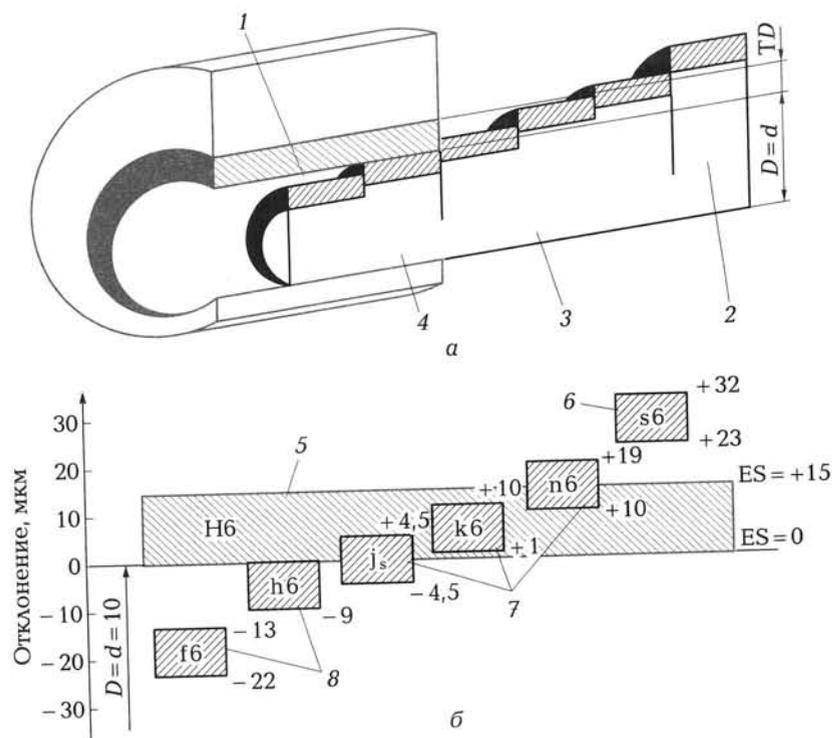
Расположение полей допусков отверстий и валов в системе отверстия (а) и схемы расположения полей допусков для различных посадок (б):
